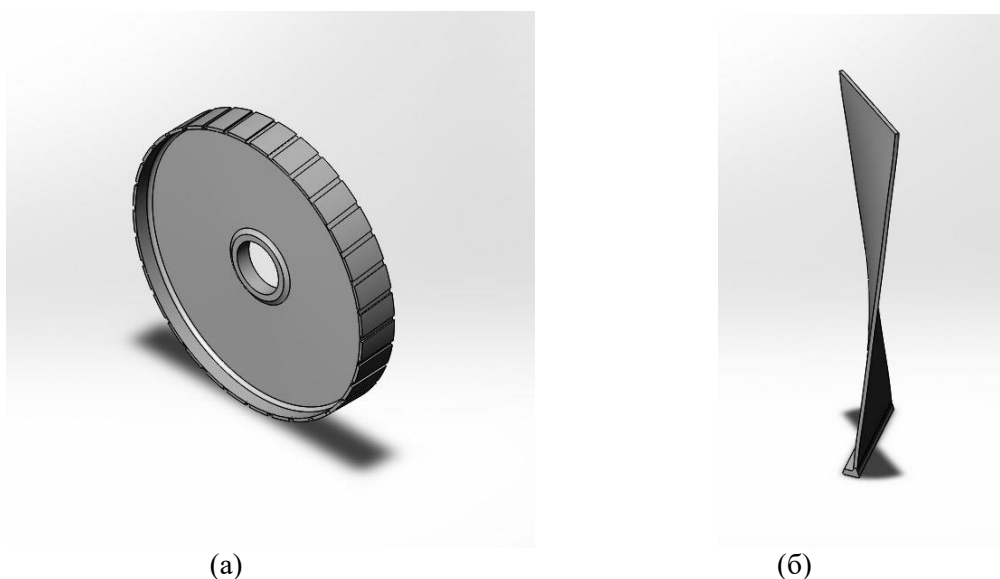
Модель диска компрессора (а) и лопатки компрессора (б)
